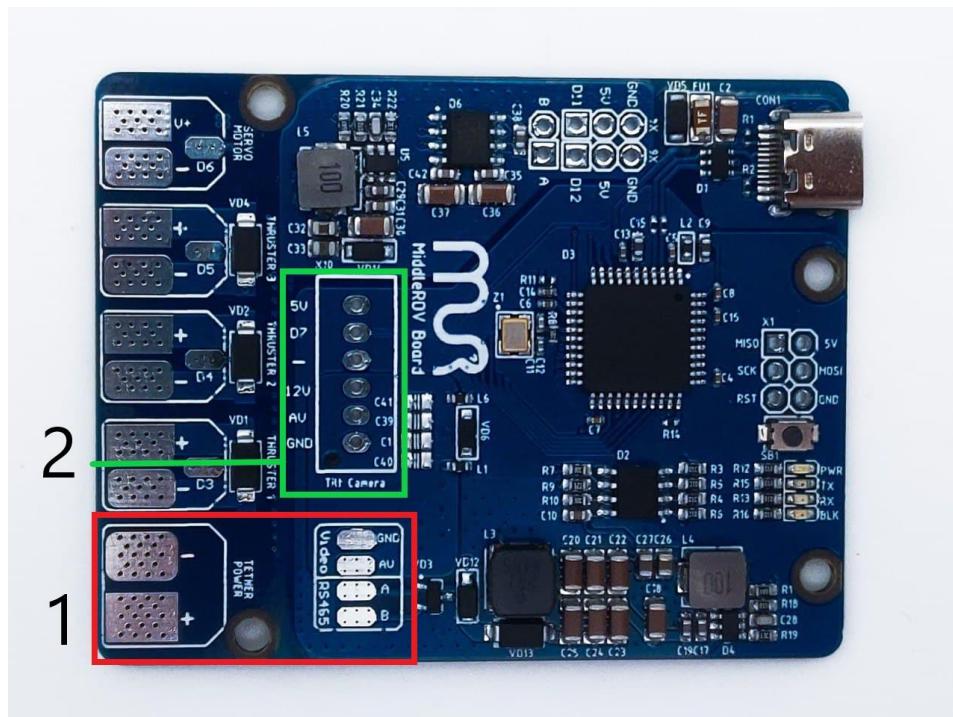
Площадки для монтажа кабель-троса (1) и поворотной камеры (2)
